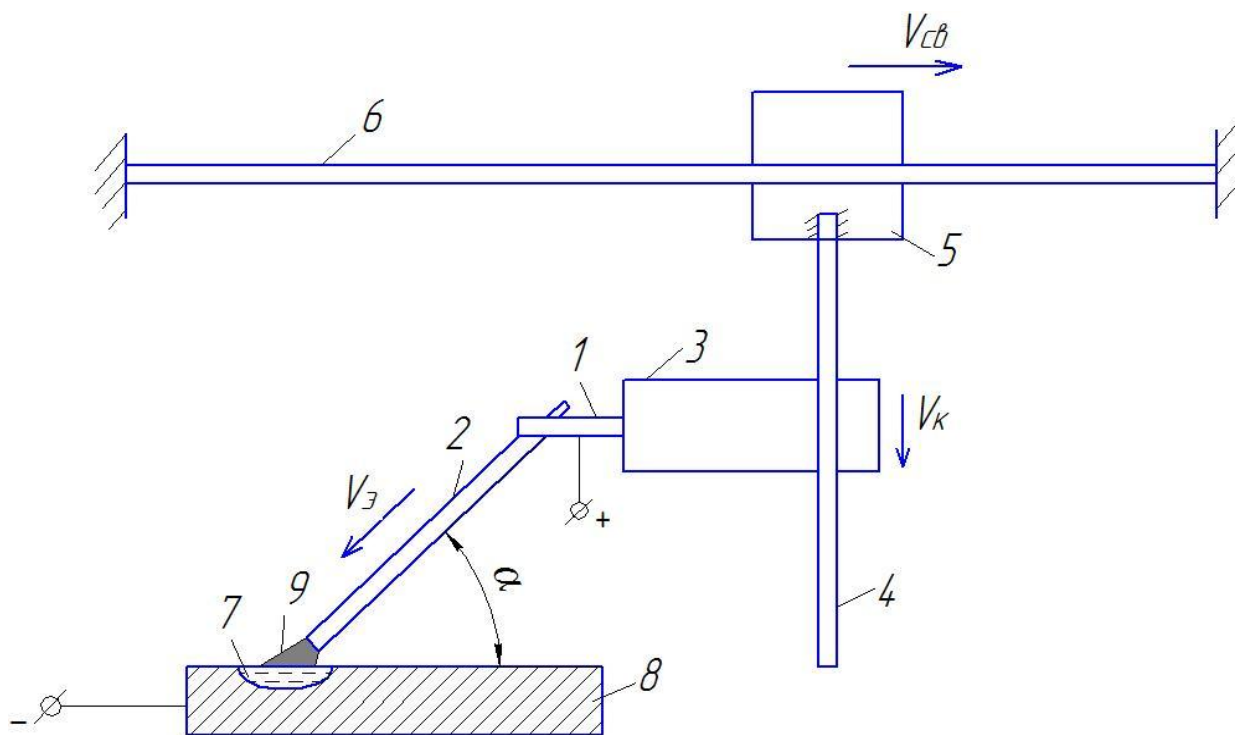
Схема реализация способа автоматической сварки
